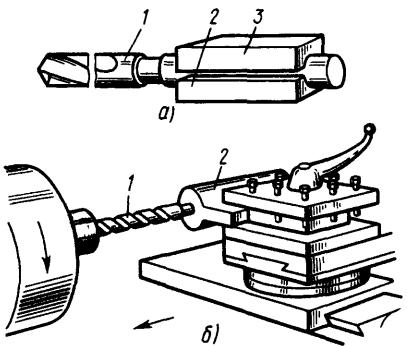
Крепление в резцодержателе сверла с цилиндрическим (а) и коническим (б) хвостовиками
